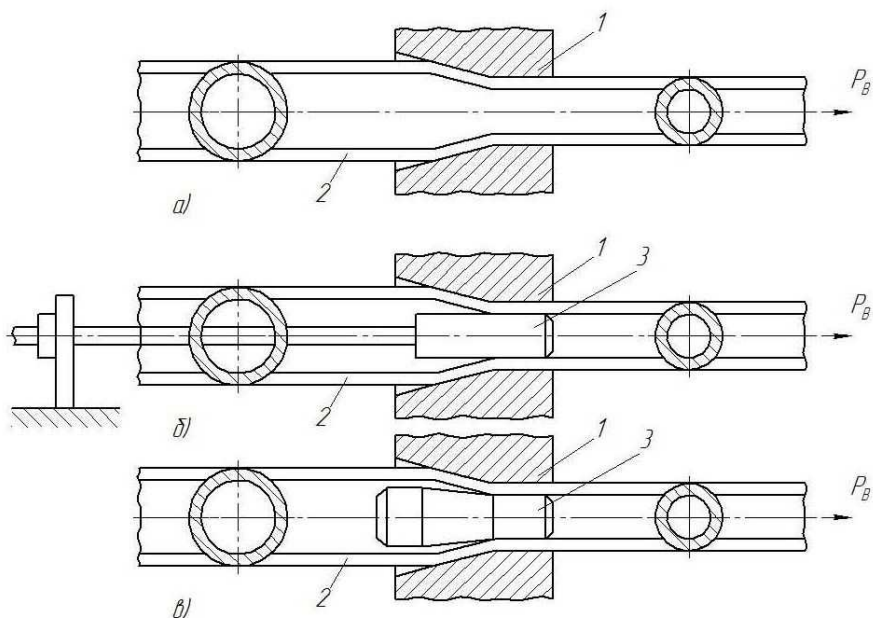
Схема волочения: 1 – волока; 2 – заготовка; 3 – оправка
